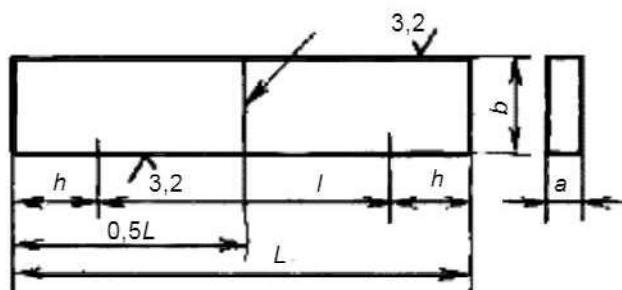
Форма зразка на розтяг зварного з'єднання [4]
